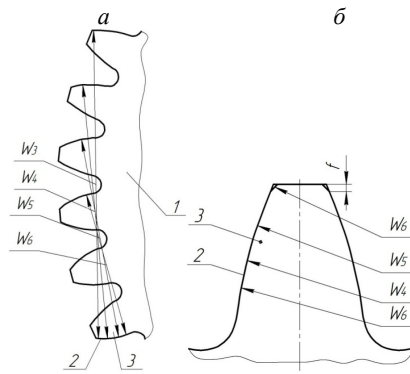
а-сектор контролируемого зубчатого колеса с расположением общих нормалей; б - один зуб колеса с расположением на его профиле точек контроля и фаски
